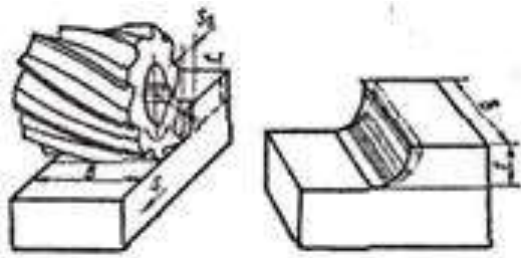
Фрезерование цилиндрической винтовой фрезой:  $B$  — ширина фрезерования,  $t$  — глубина фрезерования,  $s$  — наибольшая толщина среза.
